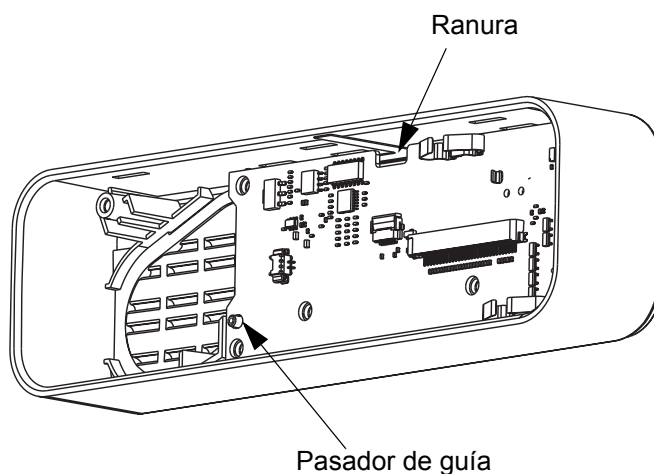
Montaje de la tarjeta en el conjunto de la unidad de control
